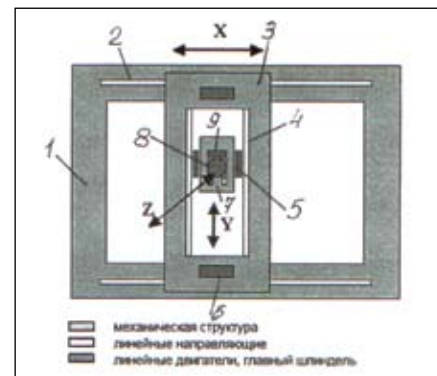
Компоновочная схема трехкоординатного обрабатывающего центра порталного типа с тремя линейными осями
